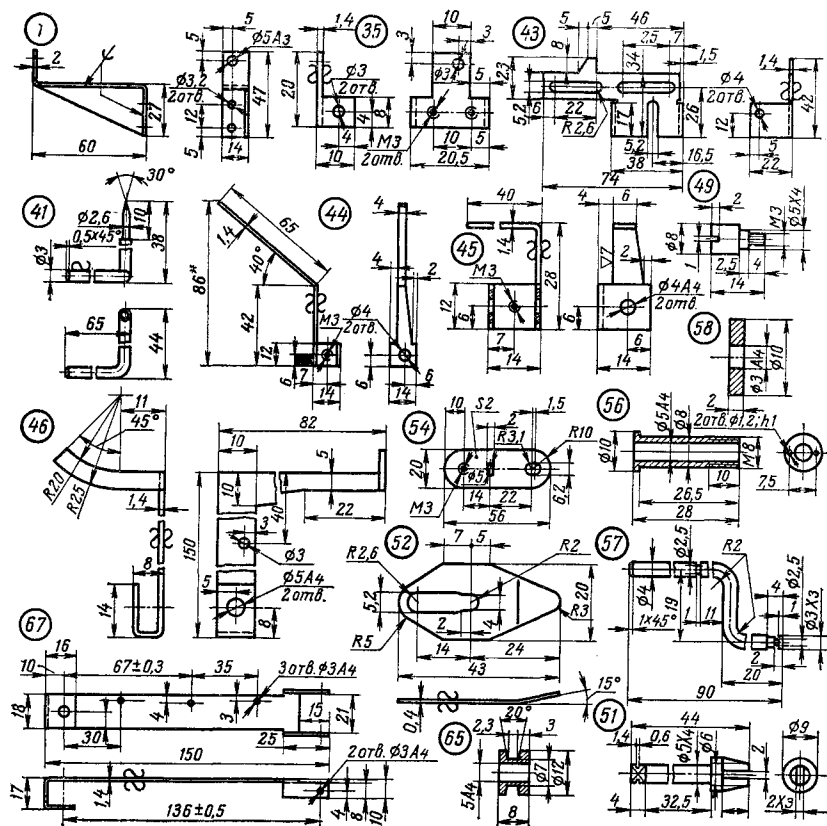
Детали переключателя формата микрофильма, механизма перемещения звуко-снимателя и узла стыковки: 1 — кронштейн, Ст.3, после пайки цинковать; 35 — скоба, Ст.3; 41 — стержень стыковочный, Ст.3; 43 — скоба, Ст.3; 44 — рычаг узла стыковки, Ст.3, закрепить на дет. 57 винтом М3×10; 45 — рычаг, Ст.3, закрепить так же на дет. 57; 46 — рычаг микрофильма, Ст.3, хромировать; 49 — поводок, Ст.3; 51 — ось ручки переключателя, Ст.3; 52 — пружина, Ст.65Г; 54 — планка переключателя, Ст.3; 56 — втулка, Ст.3, хромировать; 57 — рычаг, Ст.3; 58 — ролик, ЛС 59-1; 65 — ролик, ЛС59-1; 67 — рычаг, Ст.3. Стальные детали (кроме 1, 46 и 56) воронить.
